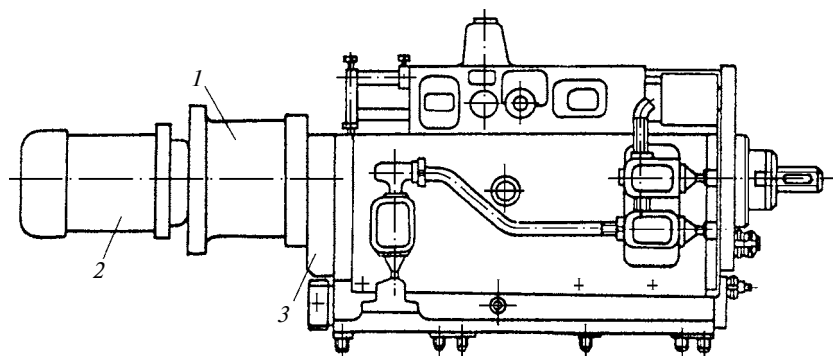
Вибропривод шпинделя силовой головки 2МУ4531 агрегатного станка
